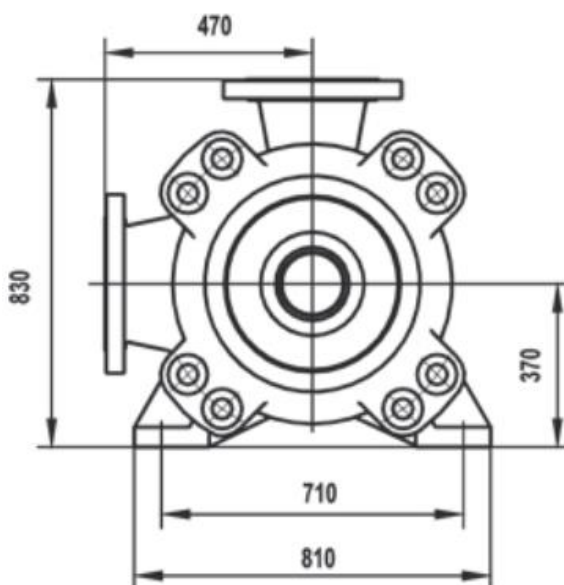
Габаритные размеры ЦНСн 315-126
